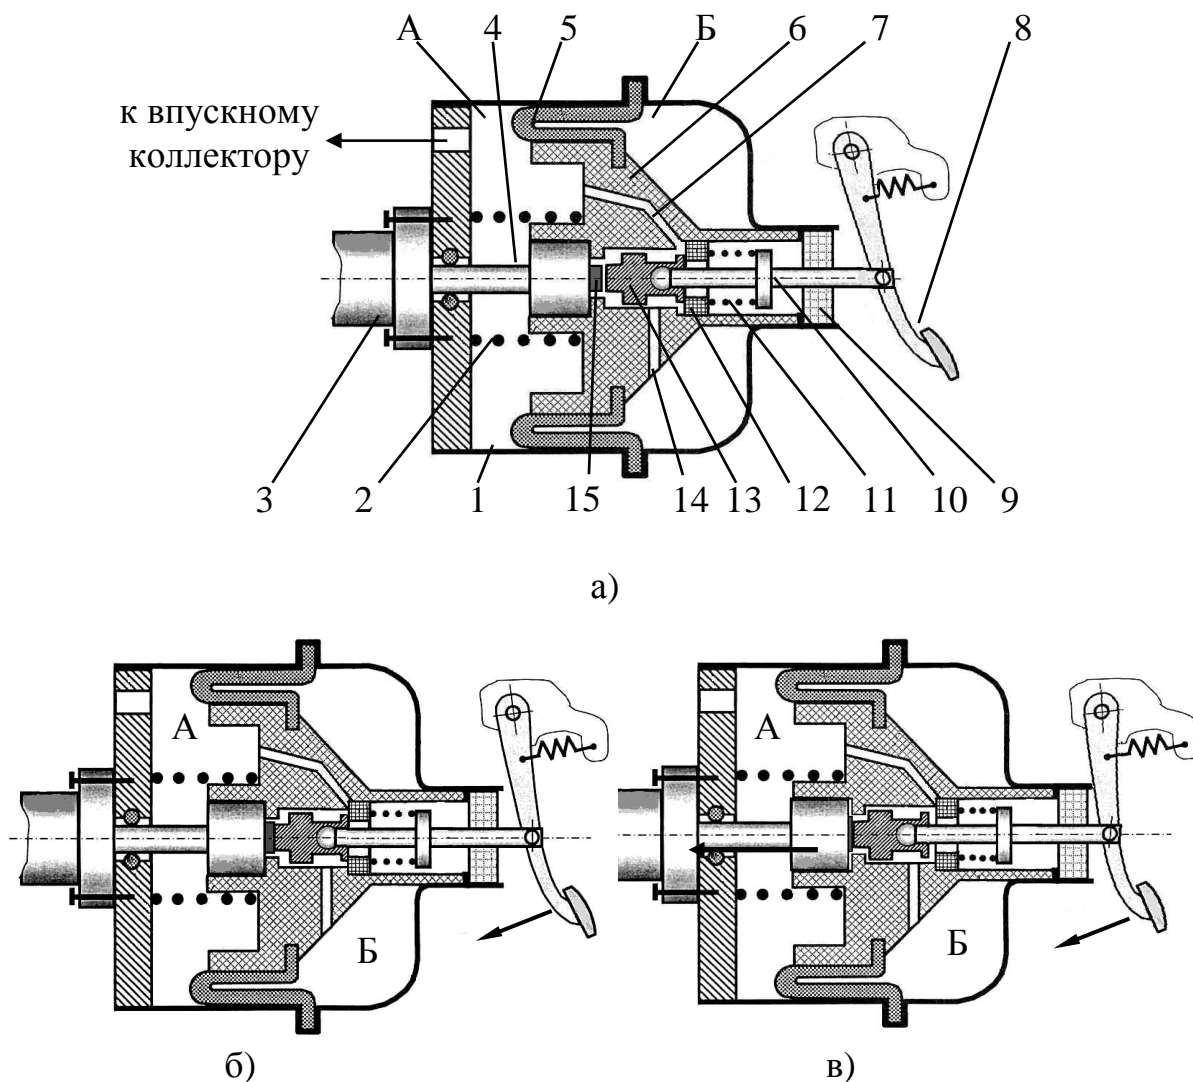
Схема вакуумного усилителя гидравлического тормозного привода: а – исходное положение, б – начало торможения, в – торможение; 1 – корпус усилителя; 2 – пружина; 3 – главный тормозной цилиндр; 4 – шток; 5 – диафрагма; 6 – поршень усилителя; 7 и 14 – каналы; 8 – тормозная педаль; 9 – фильтр; 10 – шток педали; 11 – пружина вакуумного клапана; 12 – вакуумный клапан; 13 – плунжер; 15 – упругая шайба
